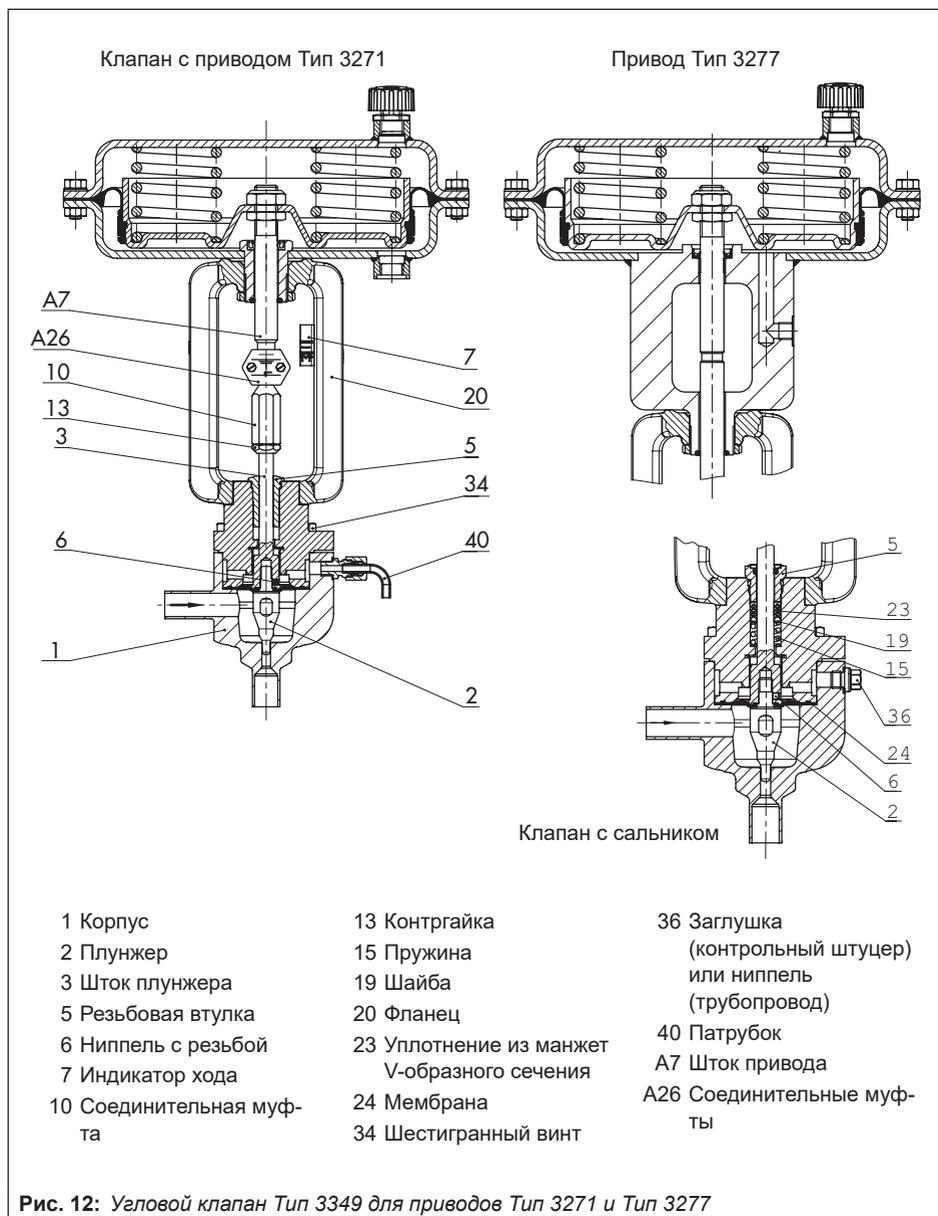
Угловой клапан Тип 3349 для приводов Тип 3271 и Тип 3277
